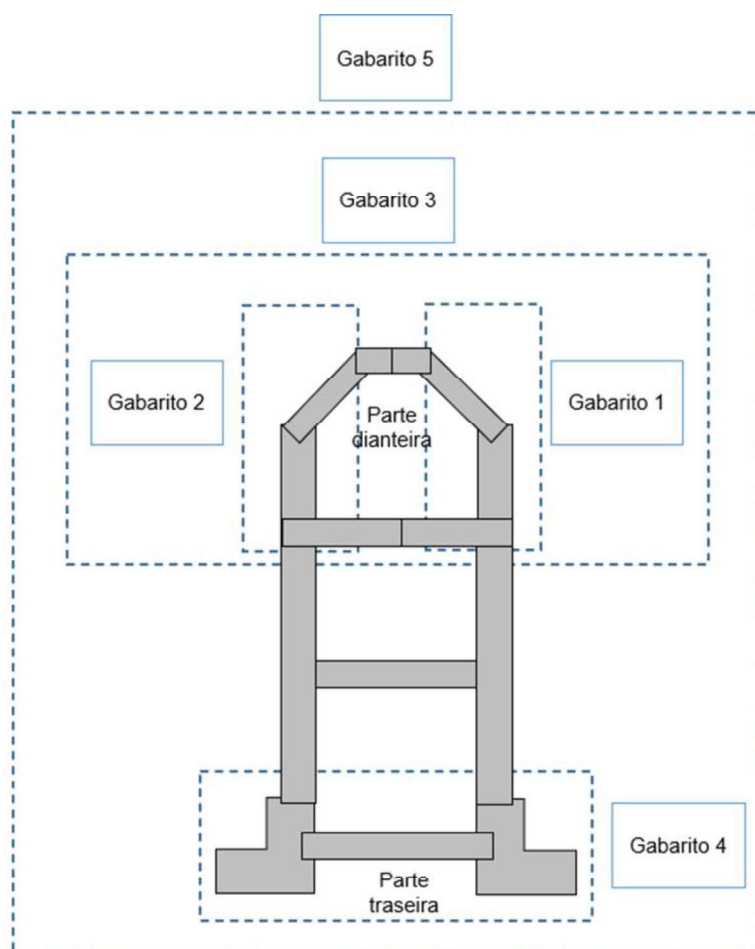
Desenho representativo do chassi de uma máquina agrícola, em vista superior, relacionando o respectivo gabarito para soldagem (Elaboração própria)
